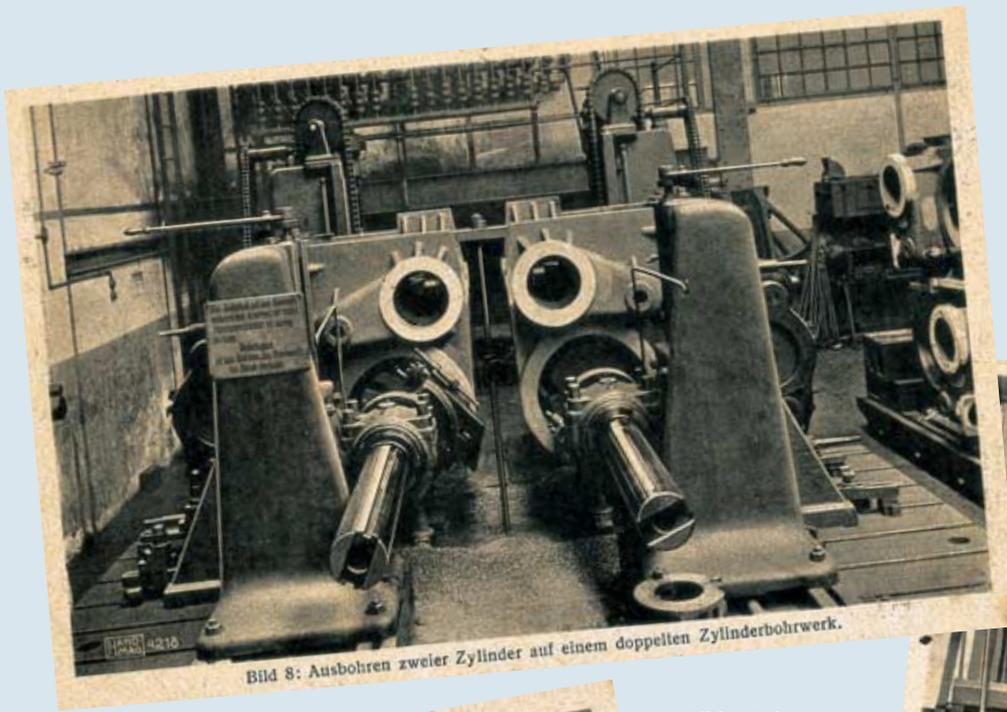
Ausbohren zweier Zylinder auf einem doppelten Zylinderbohrwerk.
